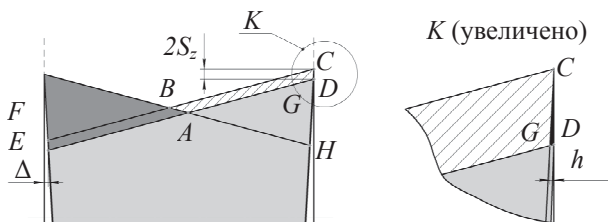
Схема формирования пропила дисковой твердосплавной пилой с попеременно-косым профилем зубьев
